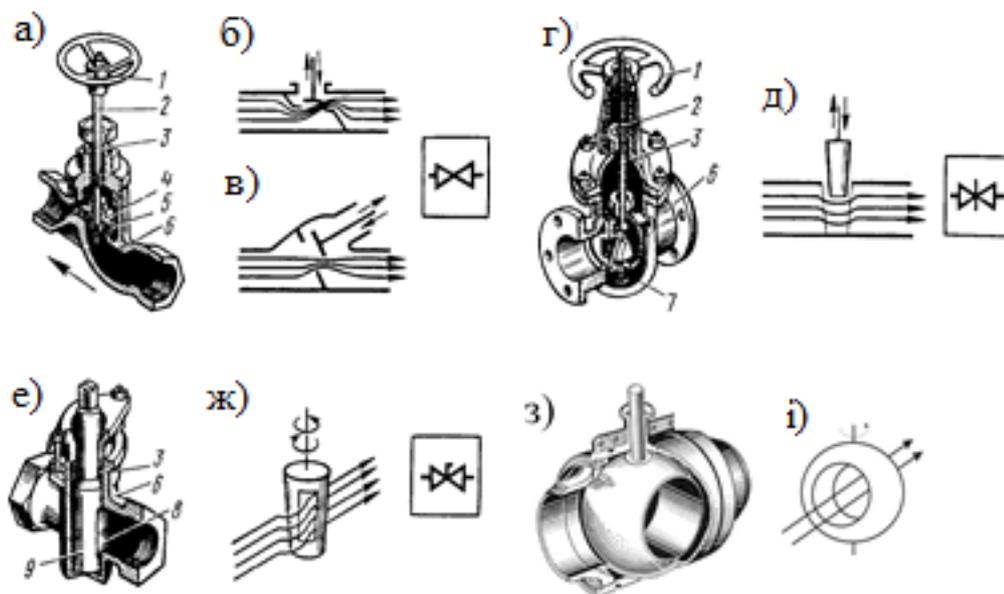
Запірна арматура: а) вентиль; б) схема прямого вентиля; в) схема вентиля «Косва»; г) засувка; д) схема засувки; е) кран корковий звичайний; ж) схема коркового крана; з) кран корковий кульовий; і) схема кульового крана
